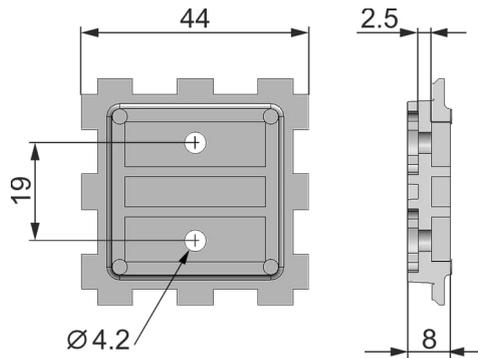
Abb. 2: Draufsicht und Querschnitt der Adapterplatte
